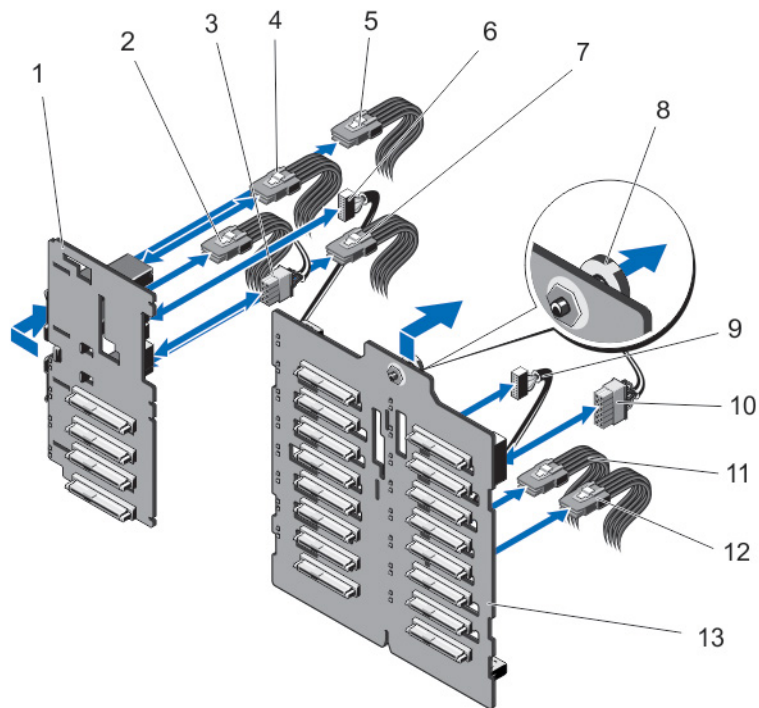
Retrait et installation de fonds de panier SAS/SATA de 2,5 pouces (x16) et de 2,5 pouces (x4)
